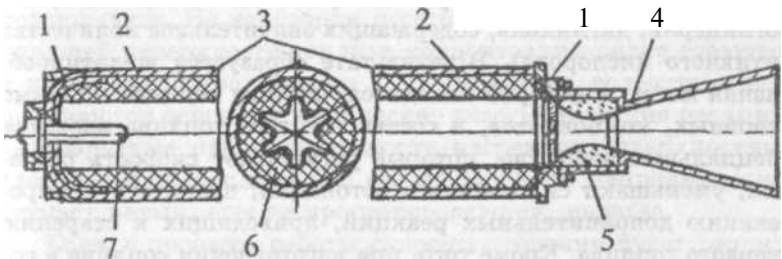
Схема ракетного двигателя твердого топлива:
